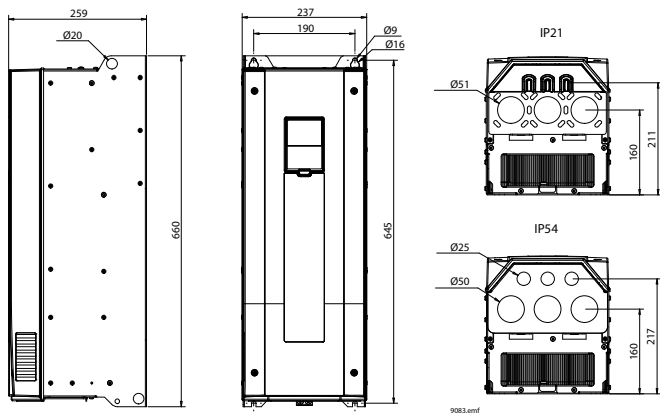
Dimensões do inversor de CA Praxi, MR7, montagem na parede
